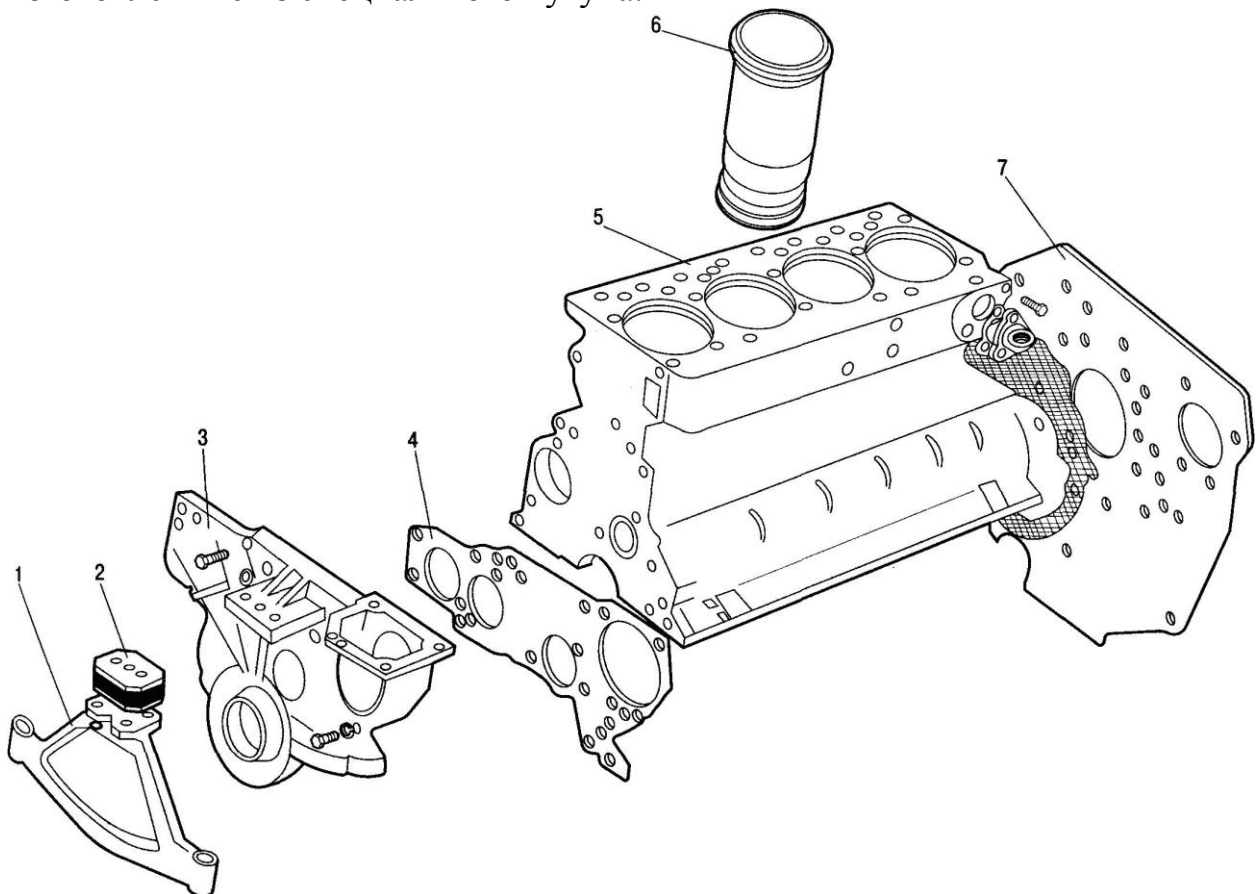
Корпусные детали дизеля: 1 - опора; 2 - резиновая подушка опоры; 3 - крышка шестерен; 4 - щит; 5 - блок цилиндров; 6 - гильза цилиндров; 7 - задний лист
